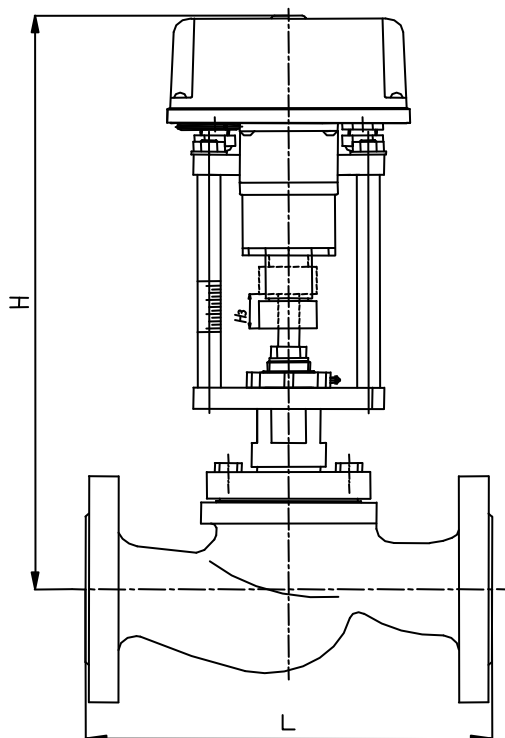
Габаритные установочные и присоединительные размеры клапана.
